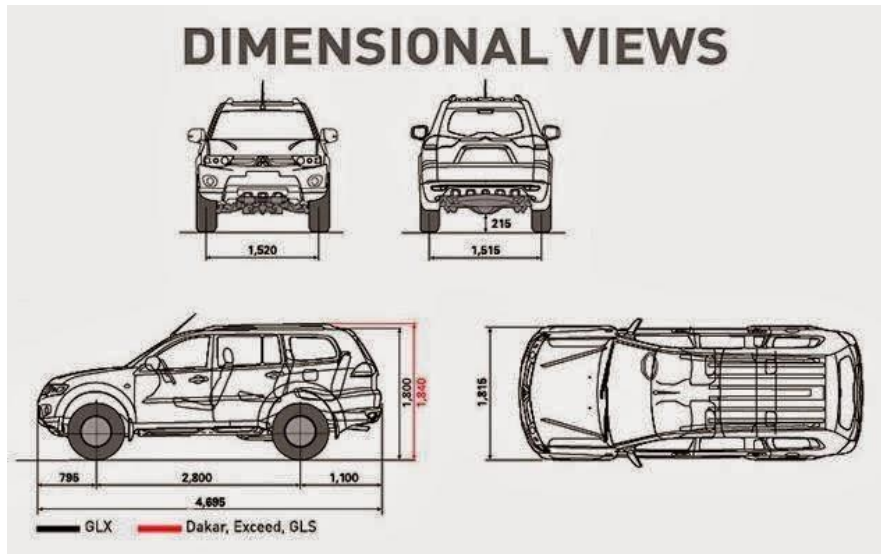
Ukuran Dimensi Mobil Outlander
